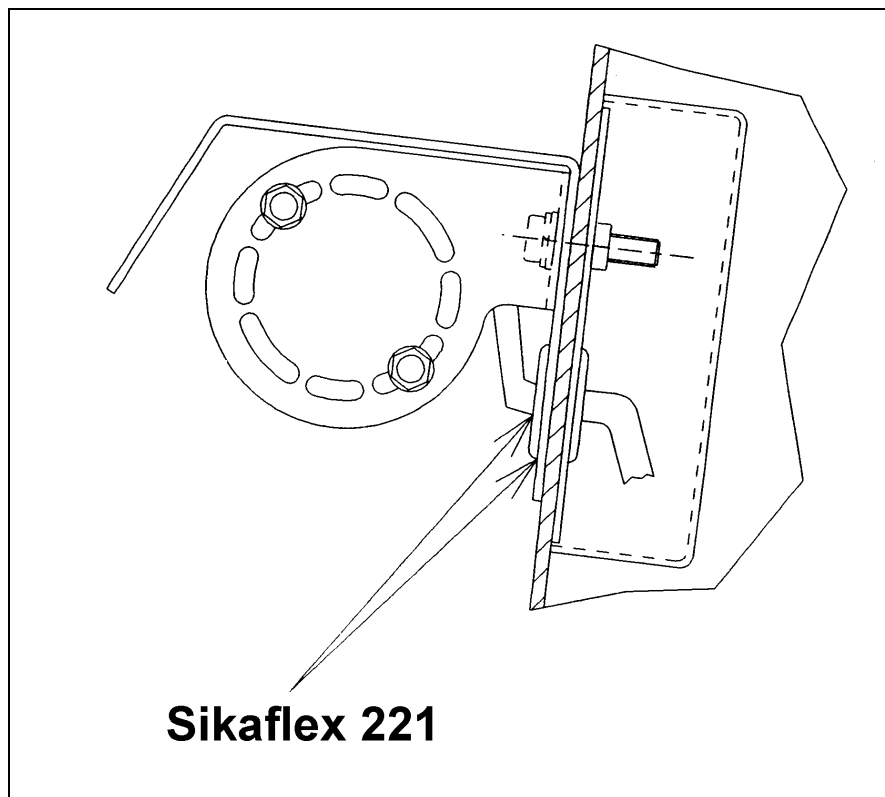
COUPE DU MONTAGE DE L'ENSEMBLE CAMÉRA
